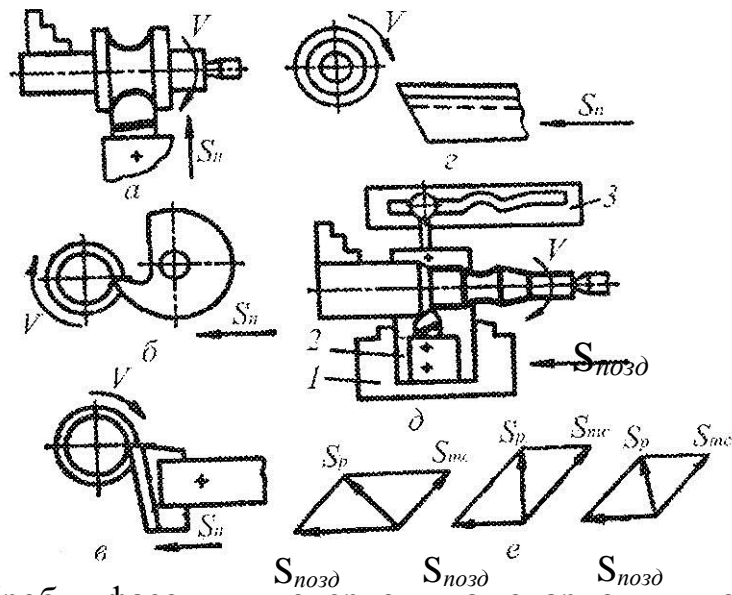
Схеми обробки фасонних поверхонь на токарно-гвинторізних верстатах
